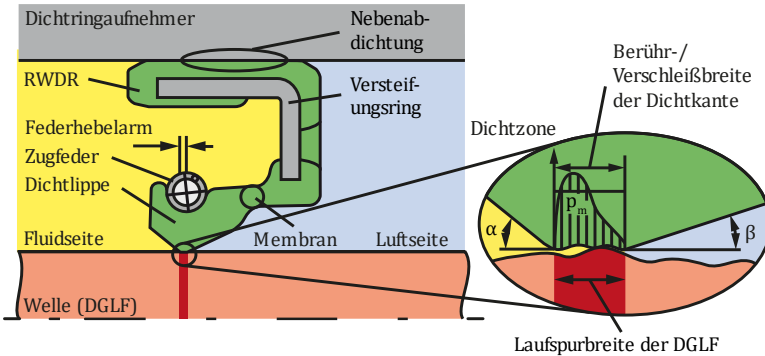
Aufbau einer Radial-Wellendichtung [10]
